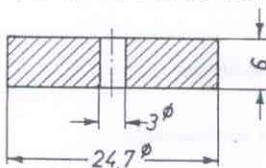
Druckstück S-1085/2 zur Selbstanfertigung für Getriebehauptwellendichtring-Auszieher S-1085
